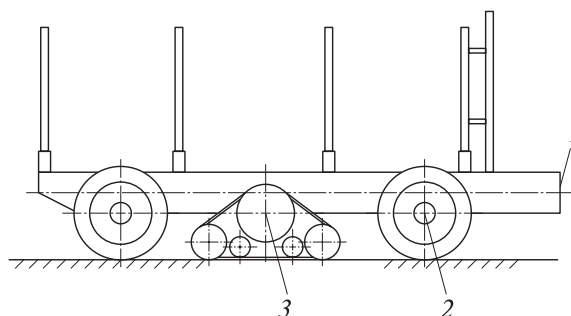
Проектируемый прицеп форвардера: 1 — прицеп форвардера; 2 — колесное шасси; 3 — гусеничный механизм
